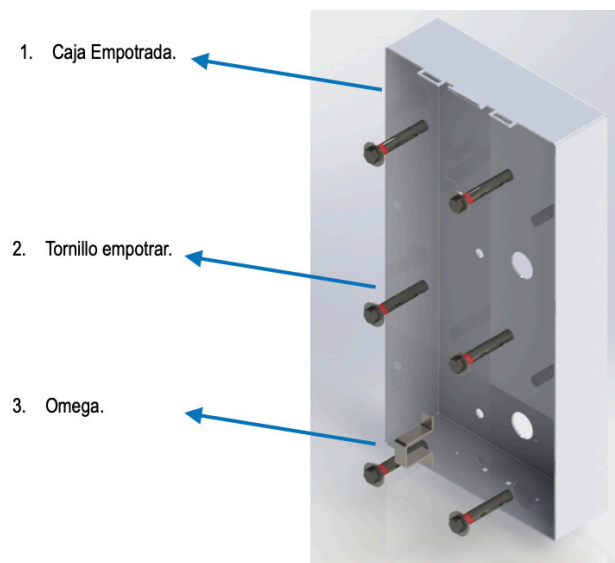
Descomposicion partes principales CAJA EMPOTRADA
